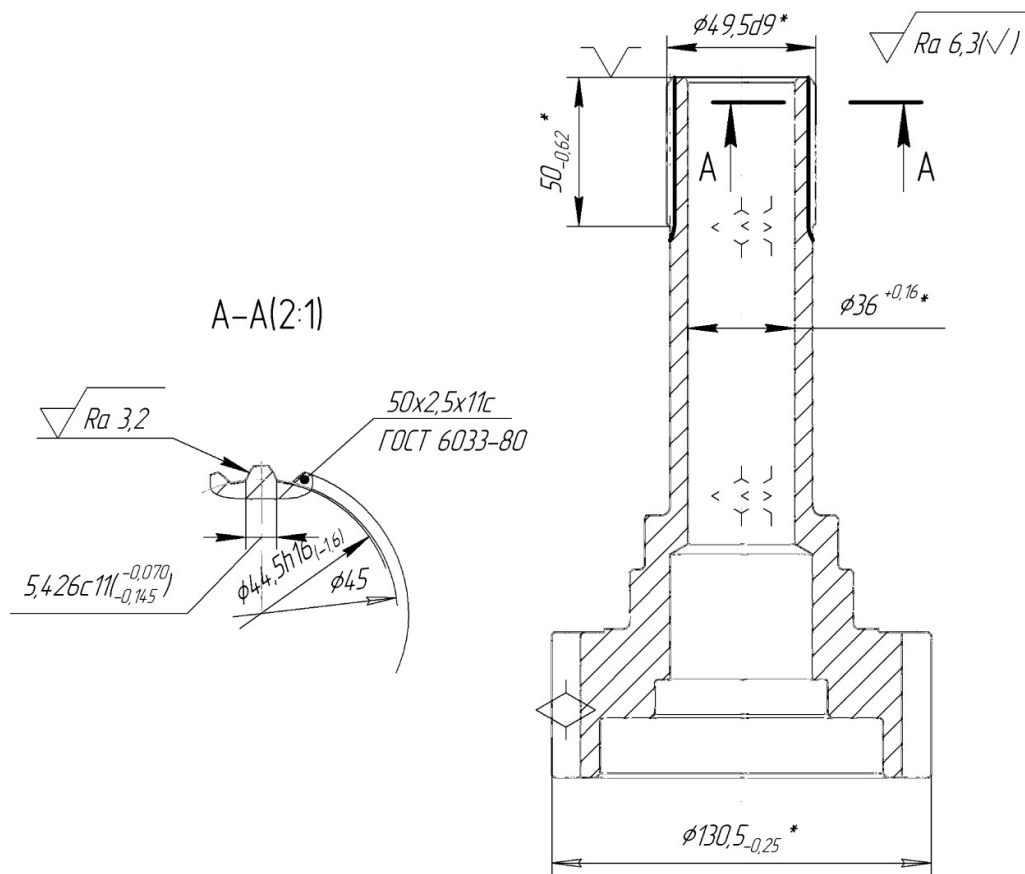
Схема базування деталі на операції 060 Шліцефрезерна
